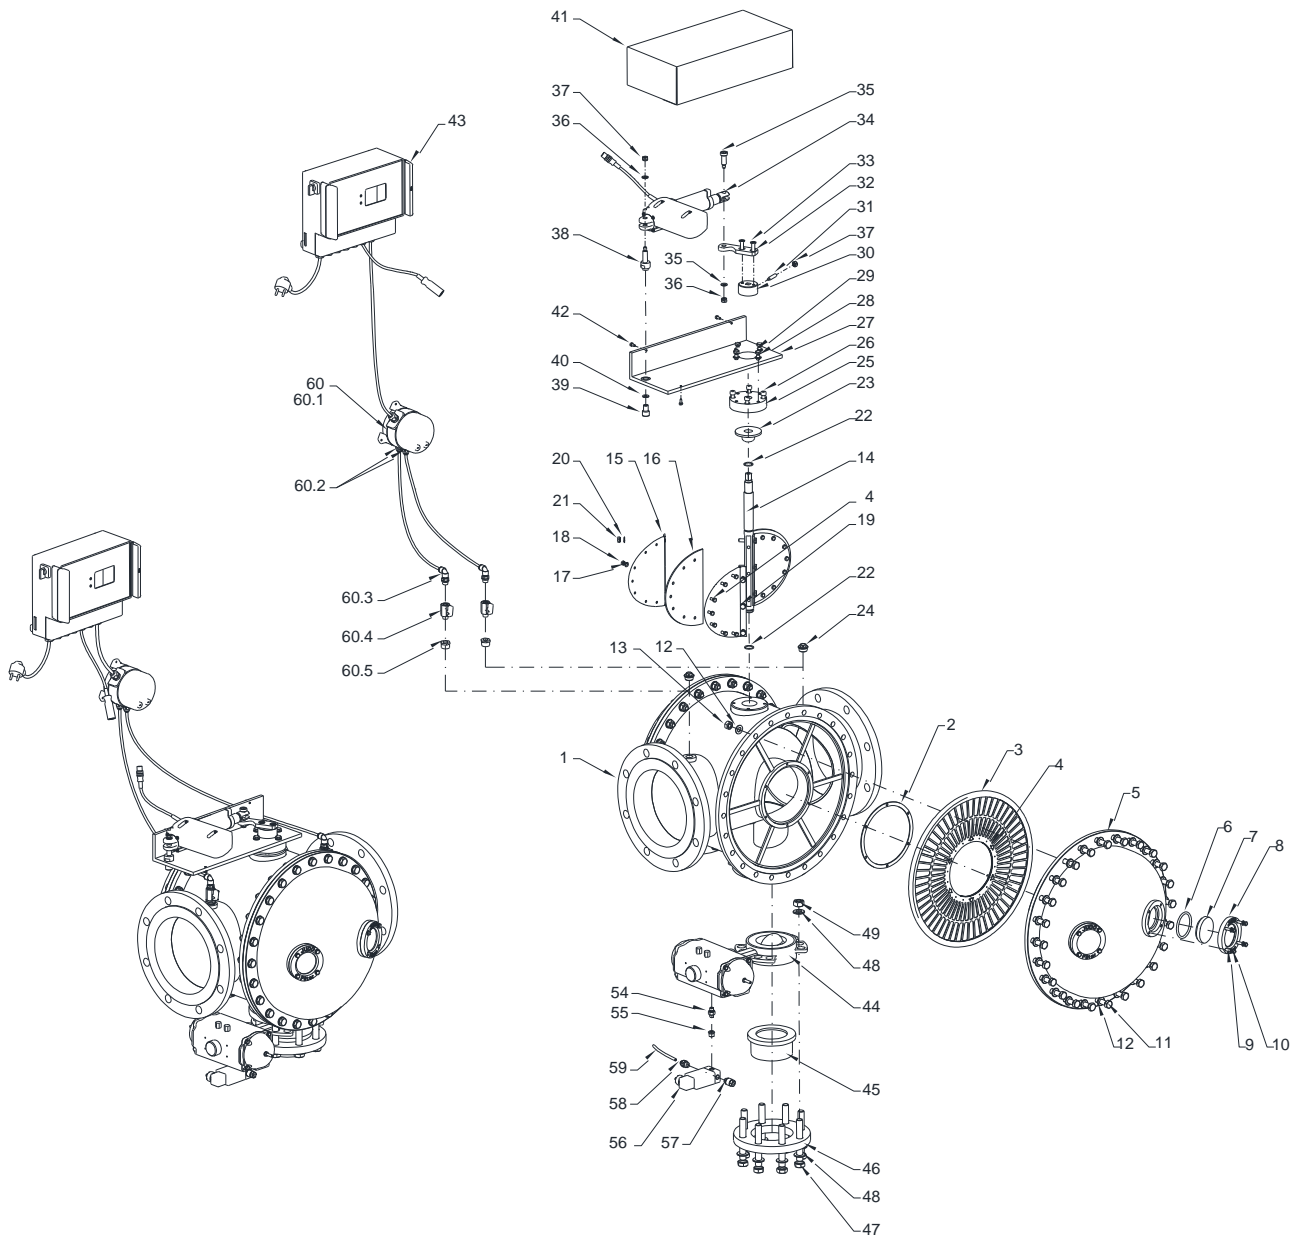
Explosionszeichnung JRSF-ATP DN200
